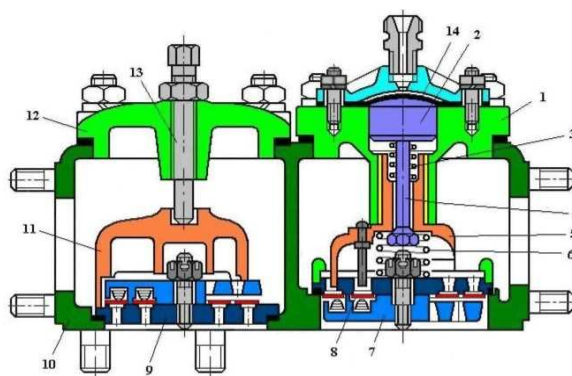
Клапанная коробка компрессора КТ-6.
